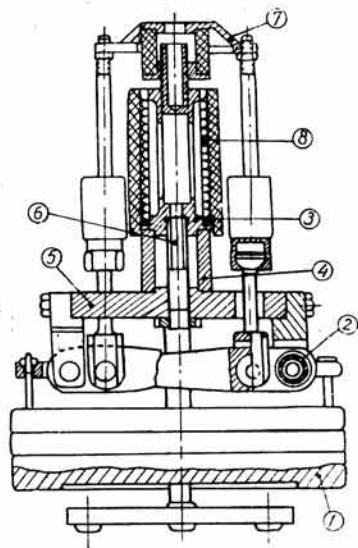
Установка для припікання у вакуумі: 1 — знімні вантажі; 2 — шарикопідшипникова опора; 3 — гніздо для укладення зразків; 4 — керамічна труба; 5 — установочна плита; 6 — порожнистий гвинт; 7 — на-вантажуюча траверса; 8 — піч опору.
